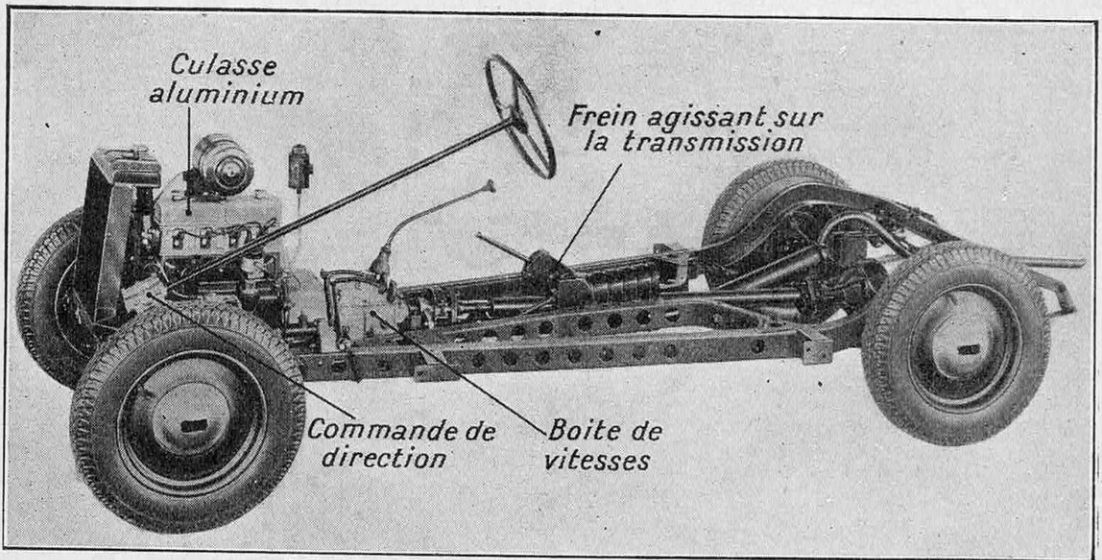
VUE D'ENSEMBLE DU CHASSIS DE LA VOITURE LÉGÈRE « SIMCA-8 »
